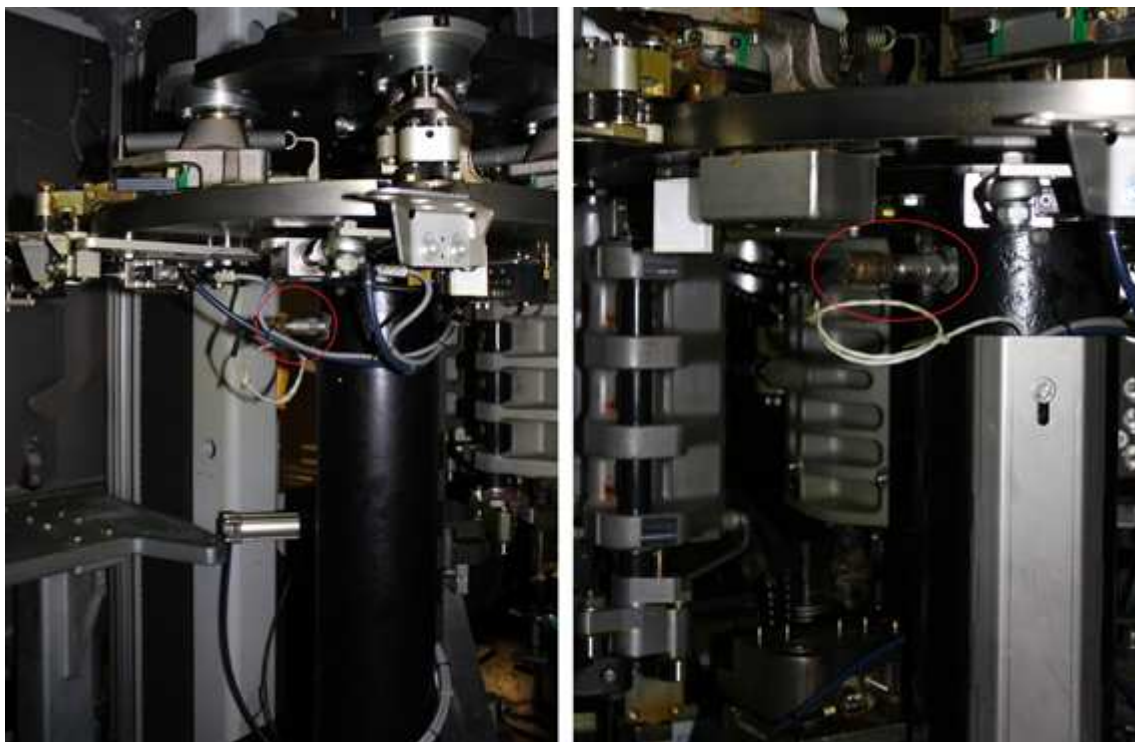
Snímače na motoru ventilátoru 1 a 2
